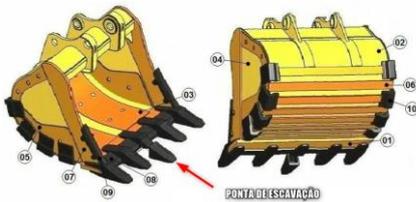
Escavadeira Hidráulica com utilização de caçamba com Pontas para Penetração do Solo.
